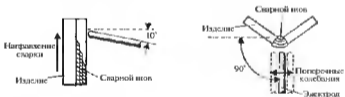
Положение электрода при сварке соединения с наружным угловым швом в вертикальном положении
